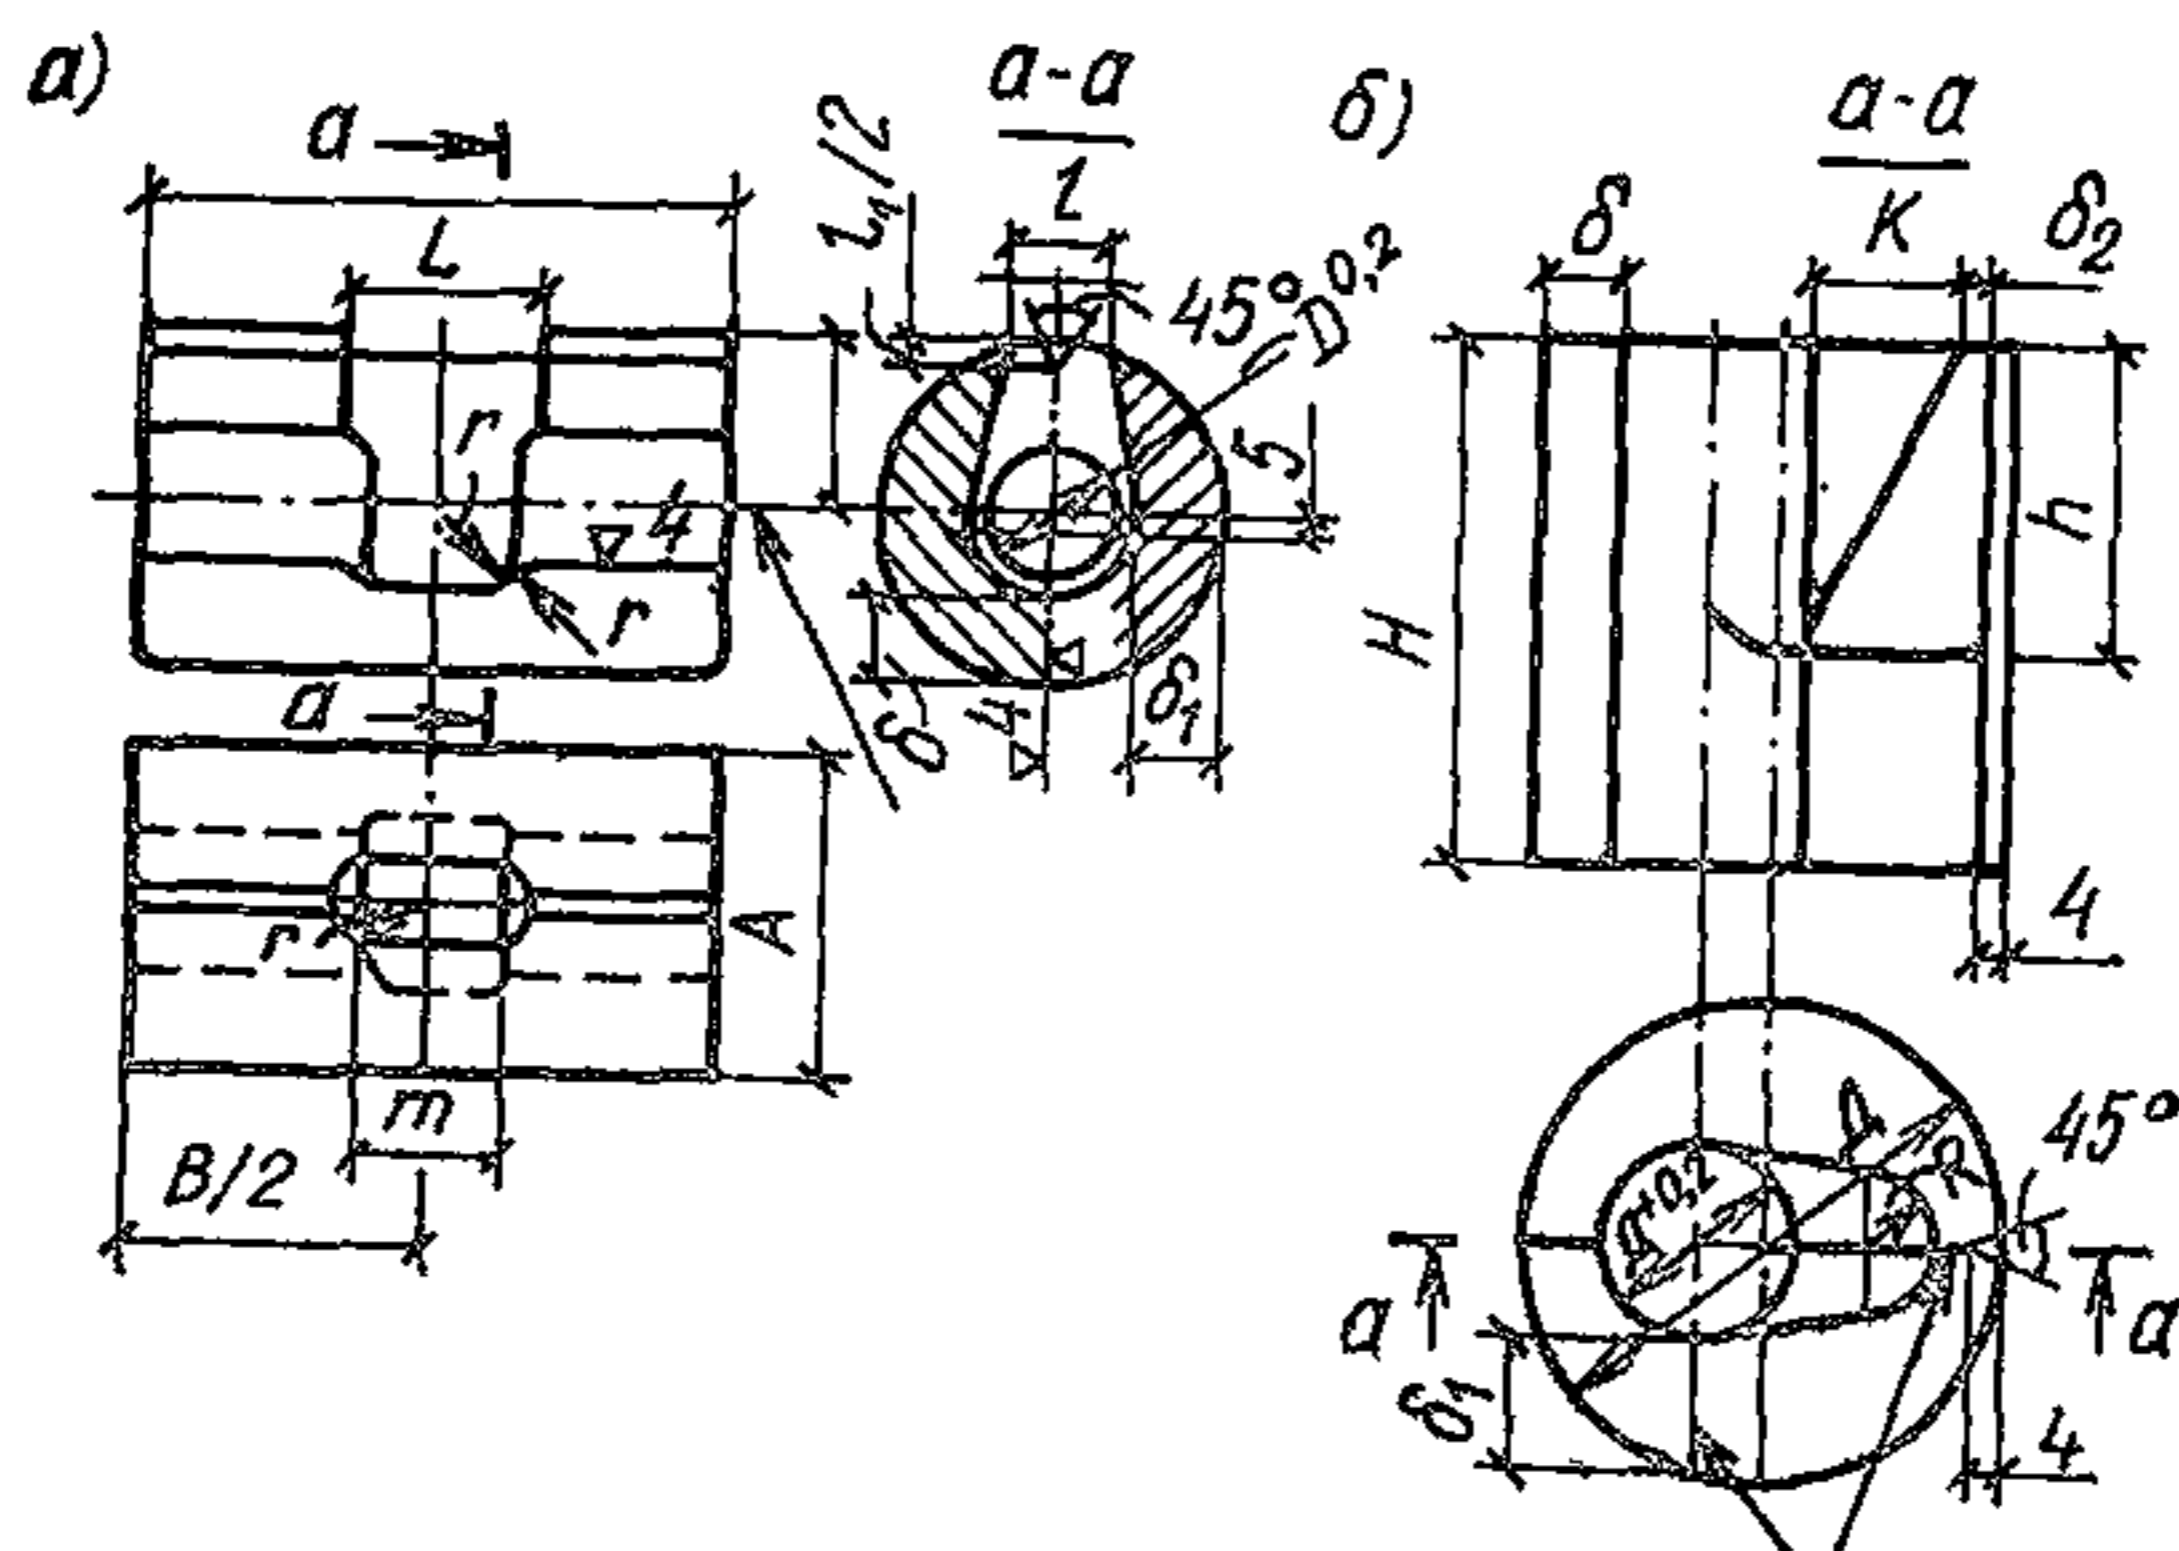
Конструкция цилиндрических инвентарных медных форм для ванной сварки стыковых соединений однорядных стержней
